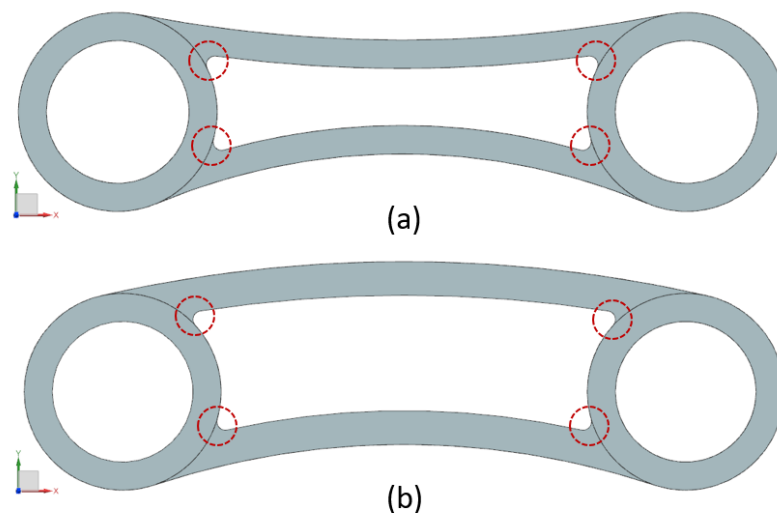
Schéma základních geometrických parametrů univerzální spojky.
